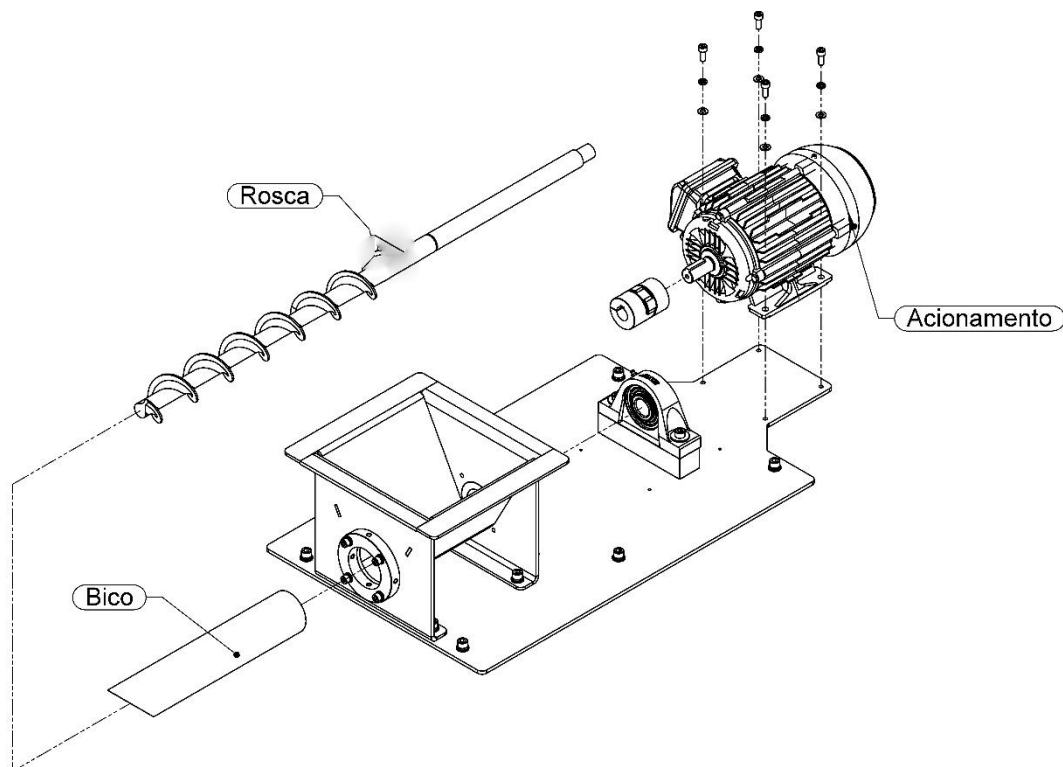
Vista explodida montagem do subconjunto dosagem.
